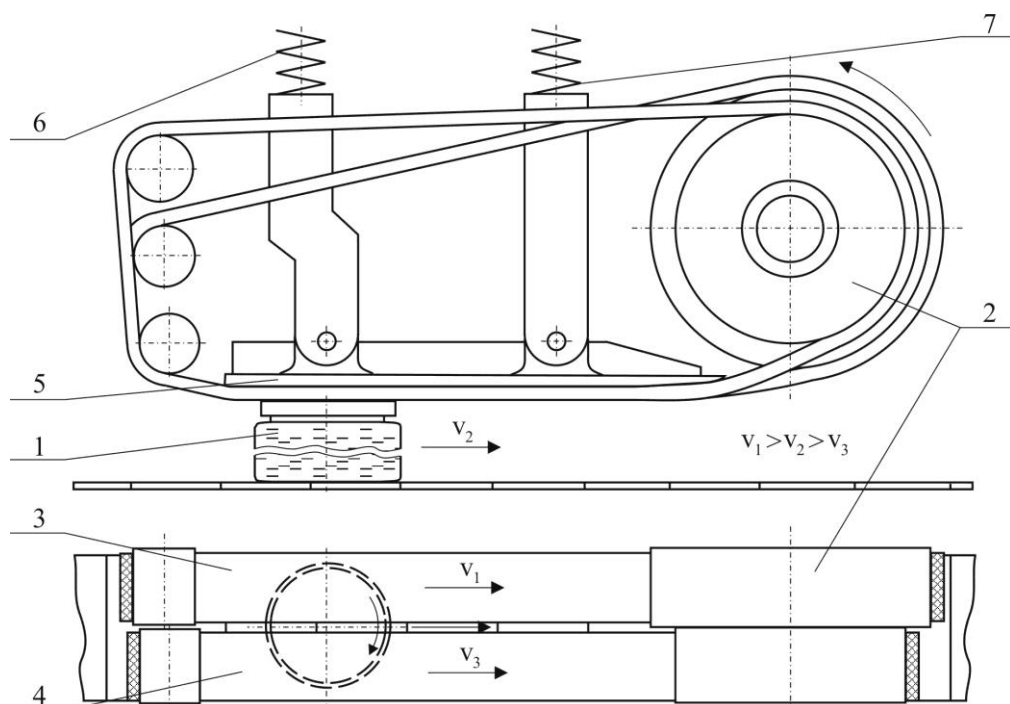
Схема механізму закупорювання машини пасового типу. 1 – банка з кришкою; 2 – привідний шків; 3, 4 – відповідно пас більшого шківа та пас меншого шківа; 5 – натискна плита; 6, 7 – регулюючі пружини.
